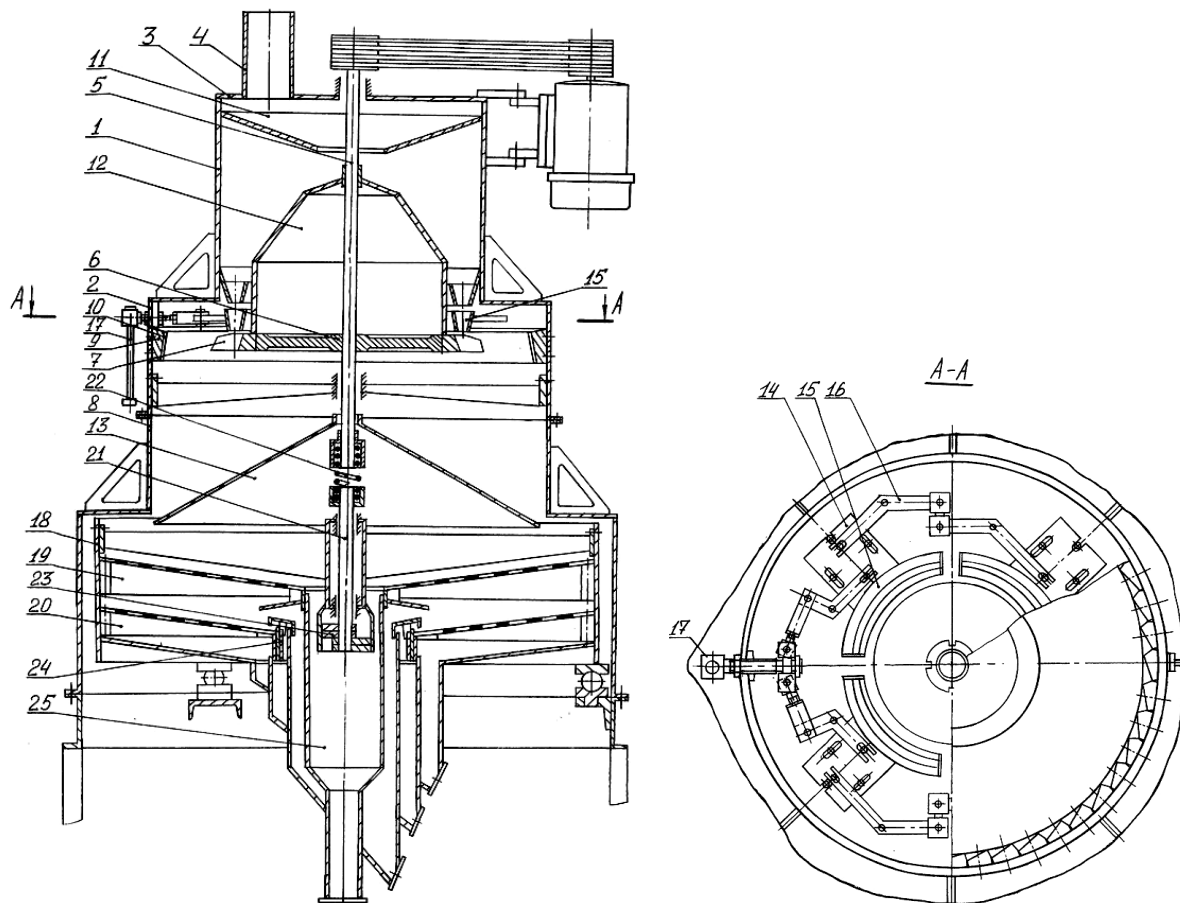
Устройство для обрушивания подсолнечных семян по патенту РФ 2162880
